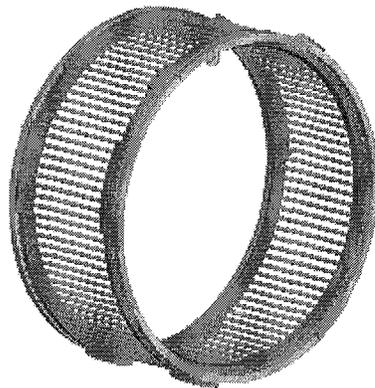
Vue d'ensemble CAO de la cage et du refroidisseur
